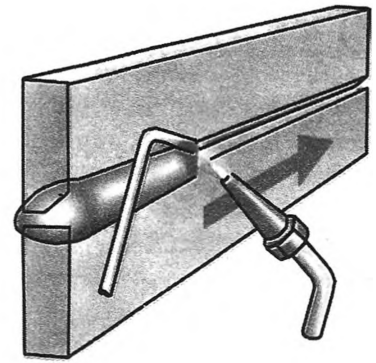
Зварювання горизонтальних швів на вертикальній поверхні
